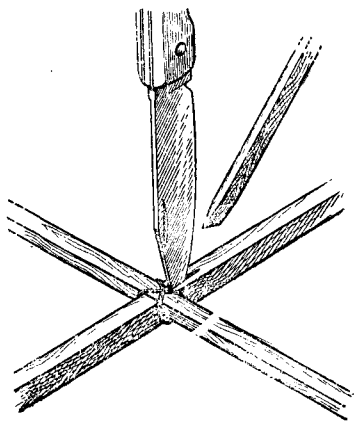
Закрепление кромок стабилизатора и кия на рейке
